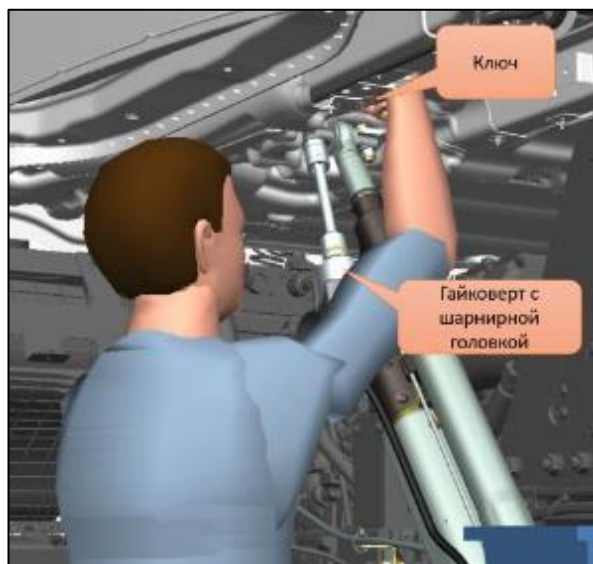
Процесс затяжки гидроцилиндра ключом и гайковертом с шарнирной головкой
